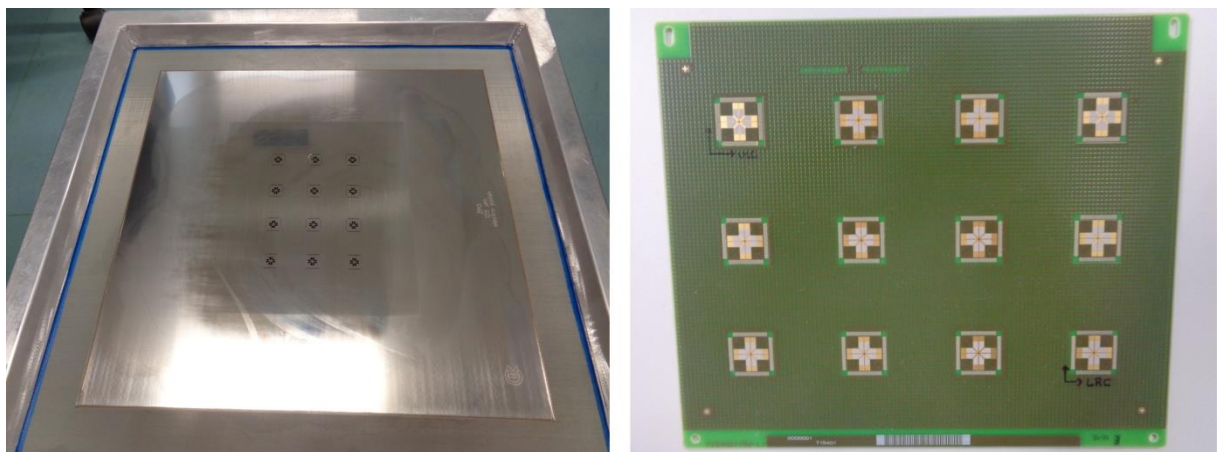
Tela (lado esquerdo) e PCB (lado direito)
